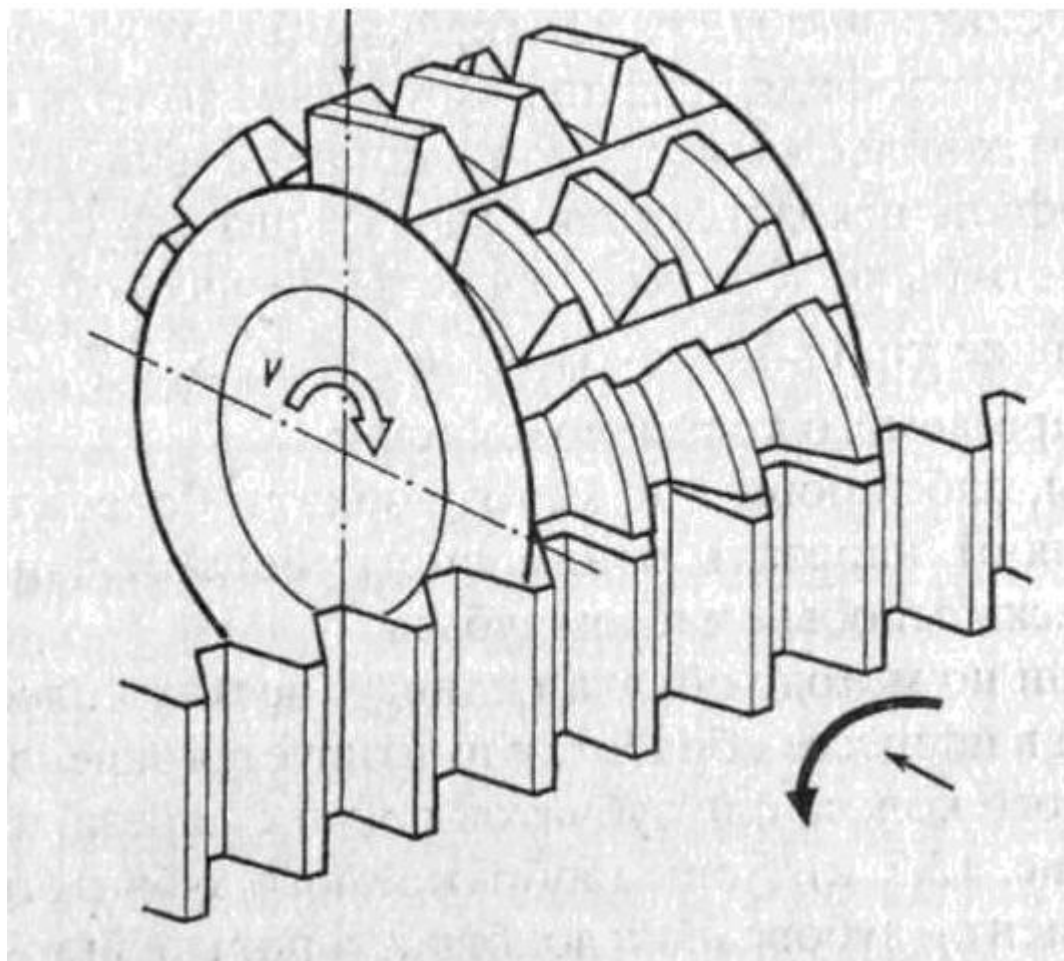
Схема зубофрезерования червячной фрезой.
